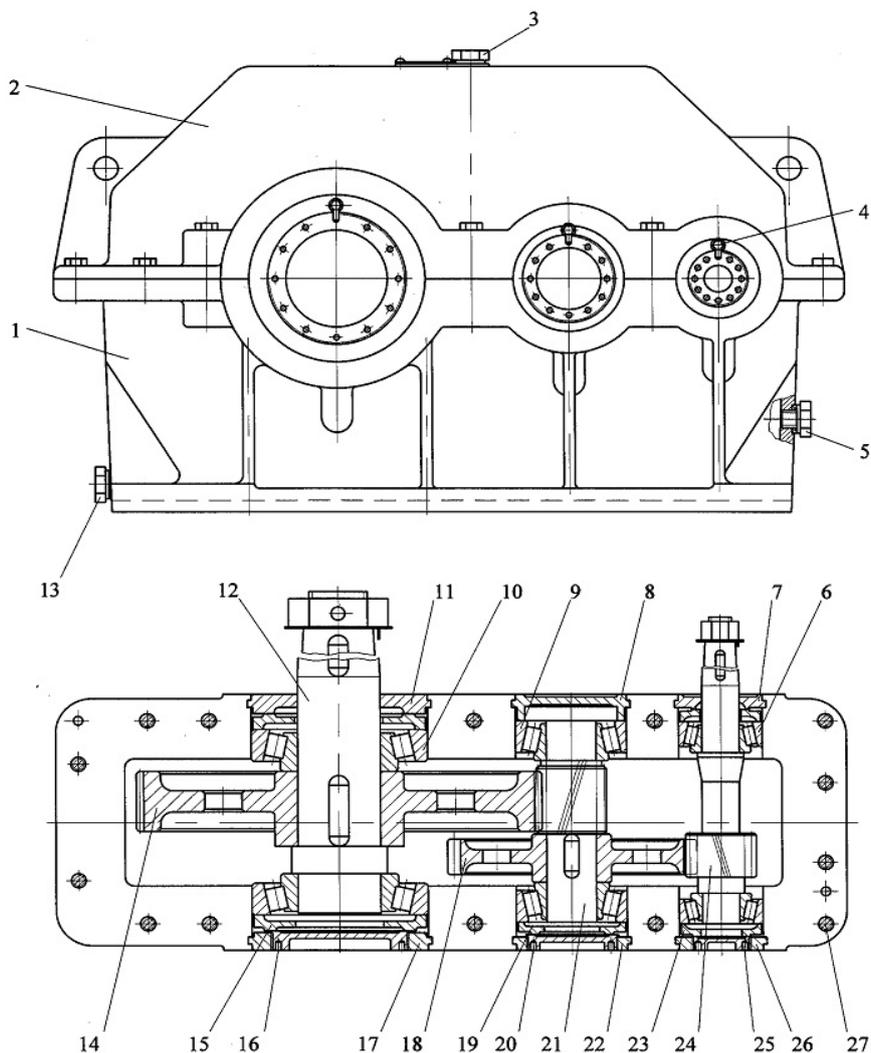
Редуктор 1Ц2У-250-31.5-22-К-У-4:
